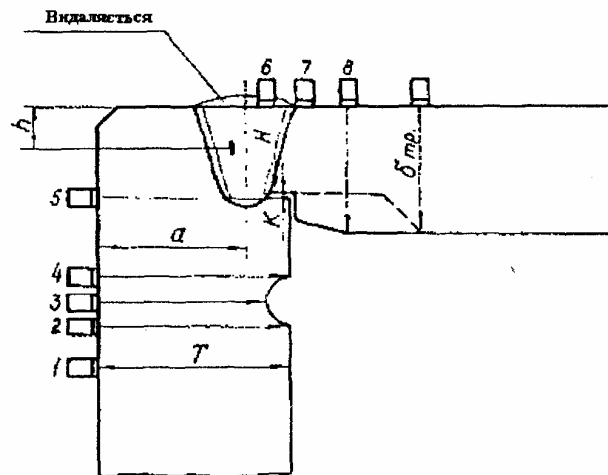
Конструкция сварного з'єднання
